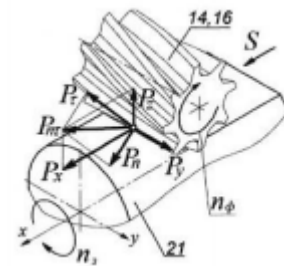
Схема дії сил різання при побіжному фрезеруванні.
